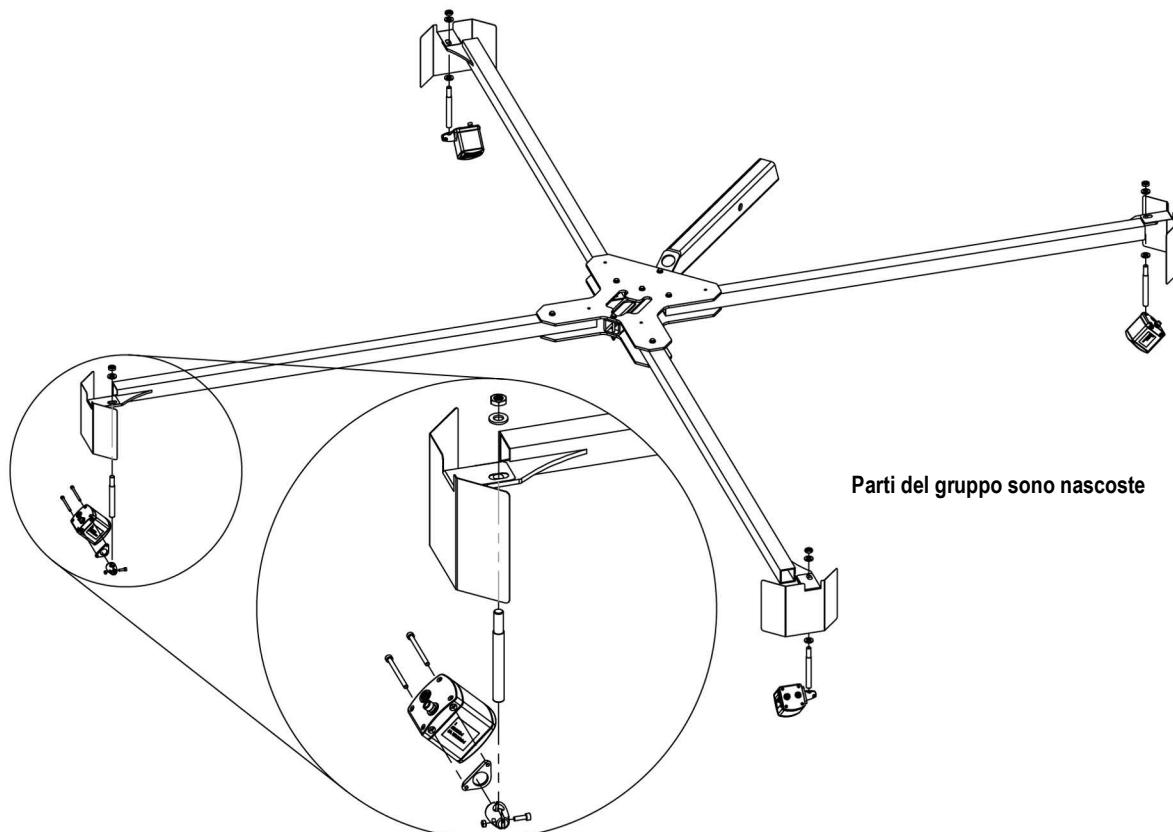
Fissaggio del gruppo sensori IFM remoti
